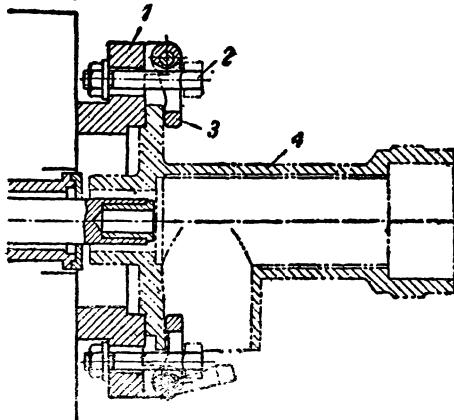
Приспособление с центрирующей выточкой и прихватами.
